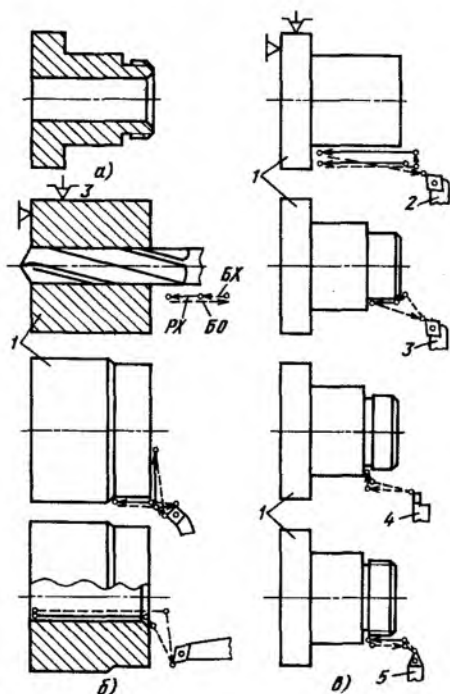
Технологический процесс обработки заготовки втулки на токарном станке с ЧПУ:
